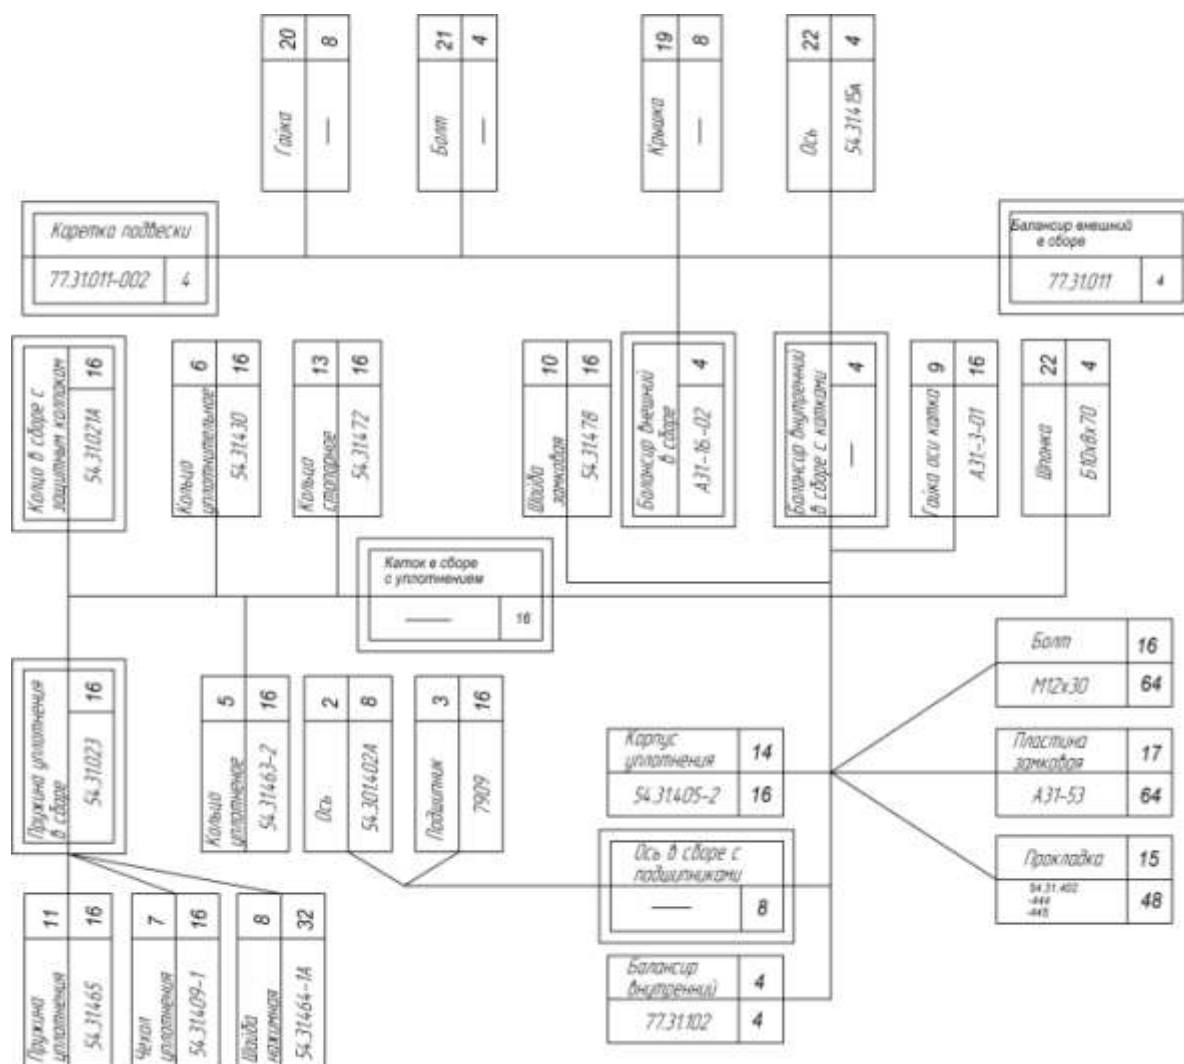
Структурная схема разборки каретки подвески трактора ДТ–75М
